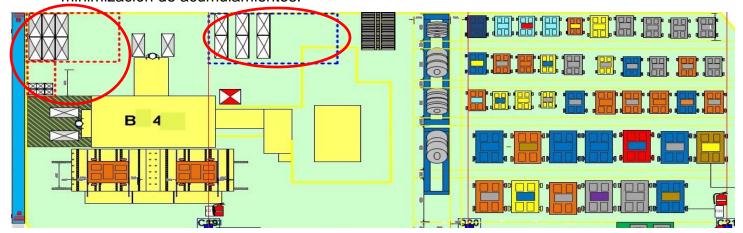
Prensa Blankin 400 Actual lay out
